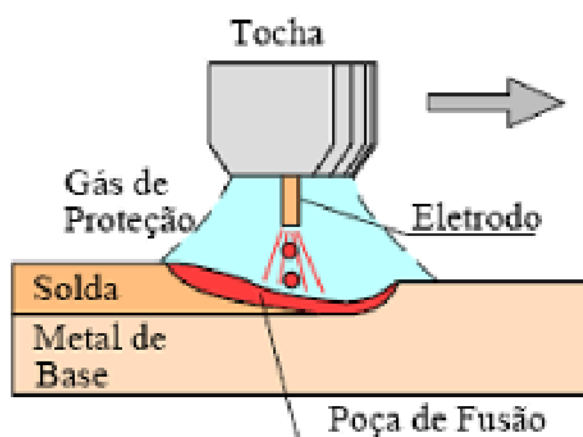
Processo de Soldagem GMAW. Fonte: MODENESI, 2000.
